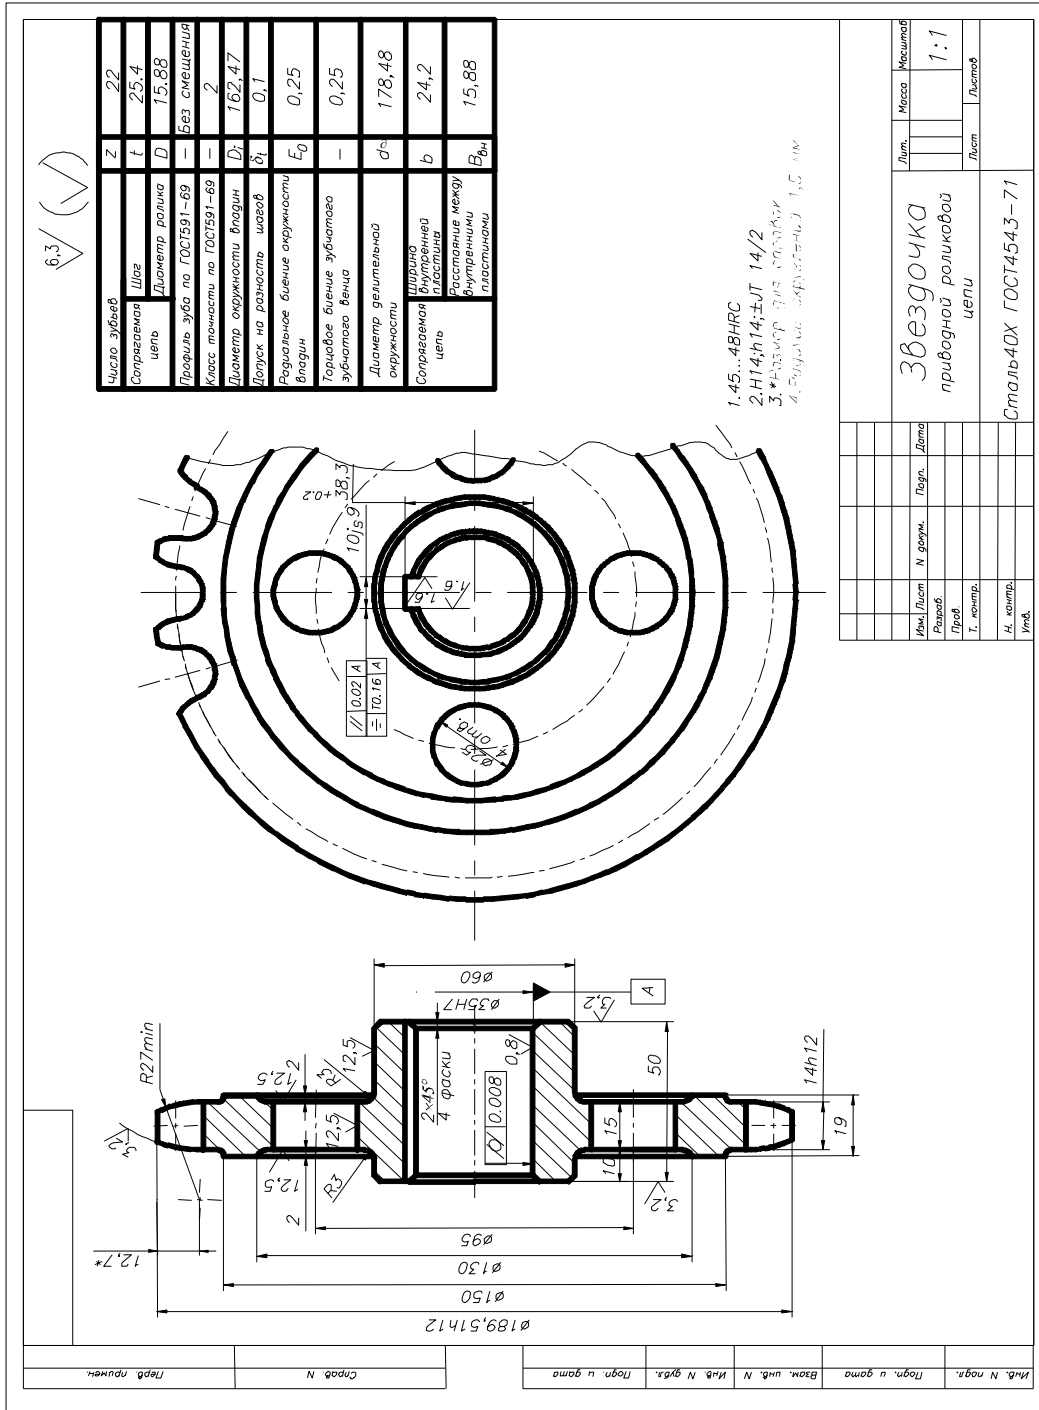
Рабочий чертеж звездочки приводной роликовой цепи
